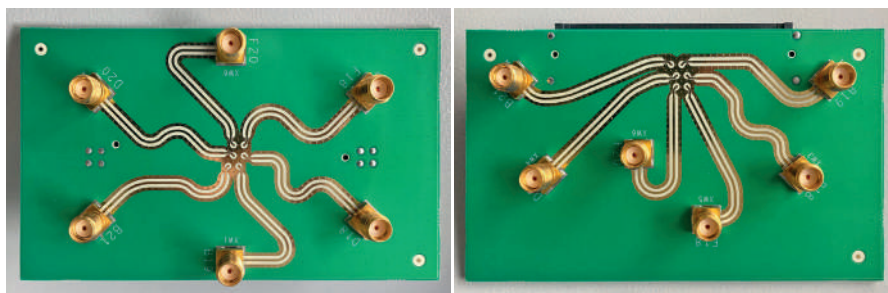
Измерительная оснастка ООО «Совтест Микро», вид снизу. Слева: плата соединителя вилка. Справа: плата соединителя розетка
